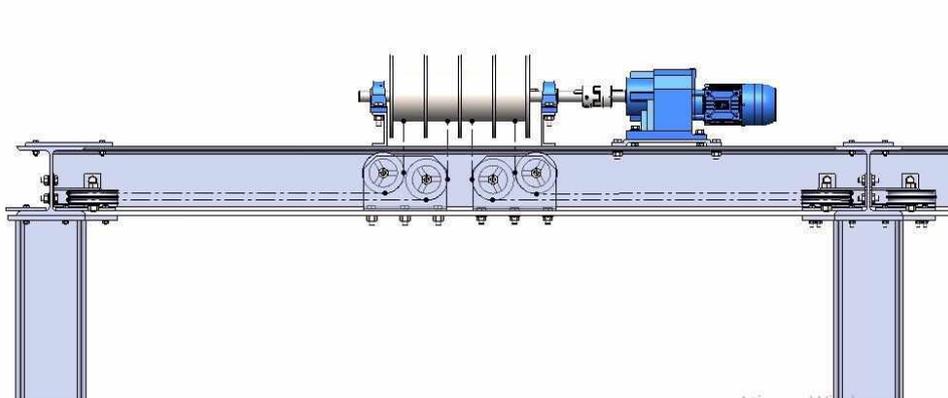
Disposição dos cabos de aço (vista de corte frontal)
